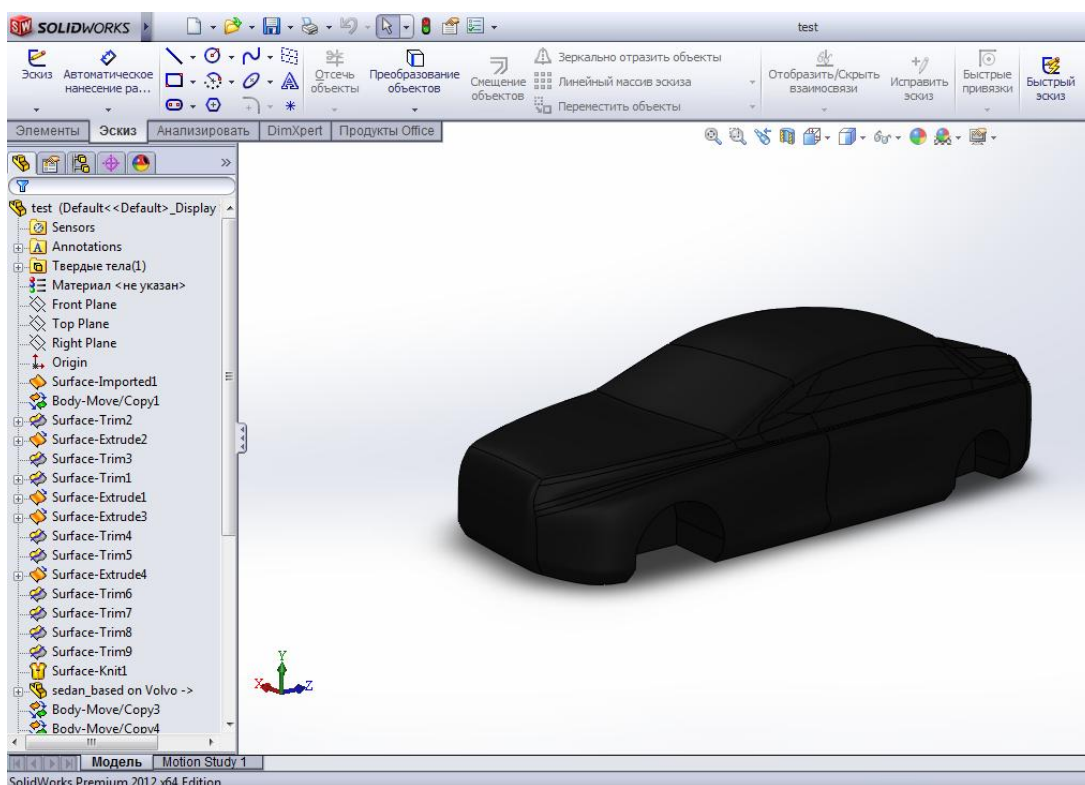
Внешний вид корпуса обдува автомобиля
